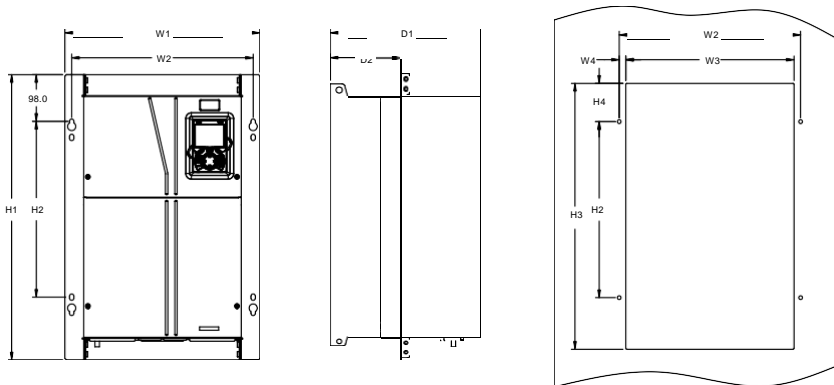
Схема ПЧ фланцевого монтажа 660 В, от 22 до 132 кВт
